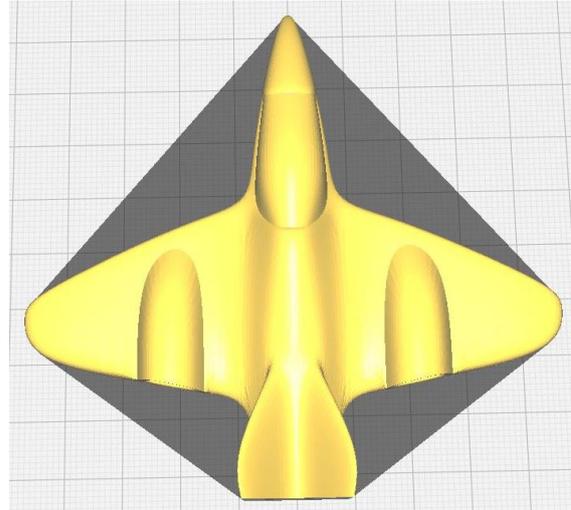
Draufsicht Testobjekt 1 - Mini-Flugzeug
